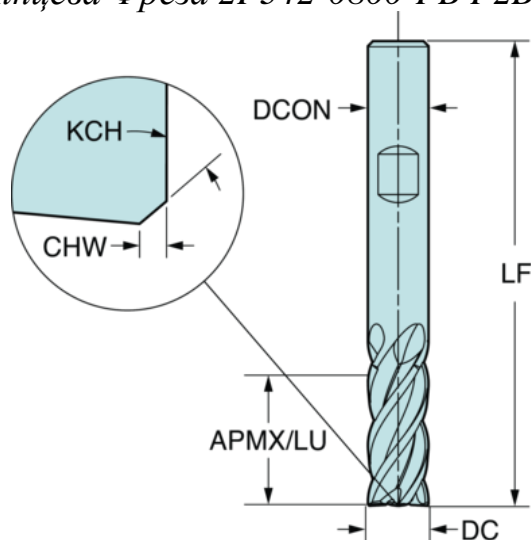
Кінцева Фреза 2P342-0800-PB P2BM
